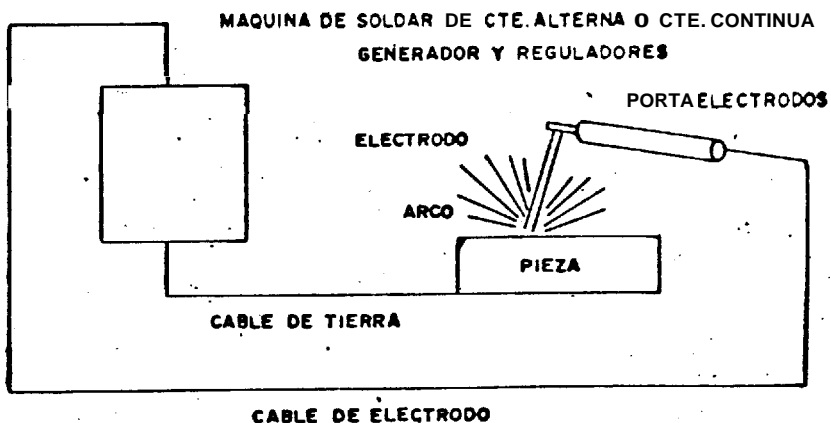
CIRCUITO DE SOLDADURA (REF. AWS. WELDING - HANDBOOK) (Ref.7)
